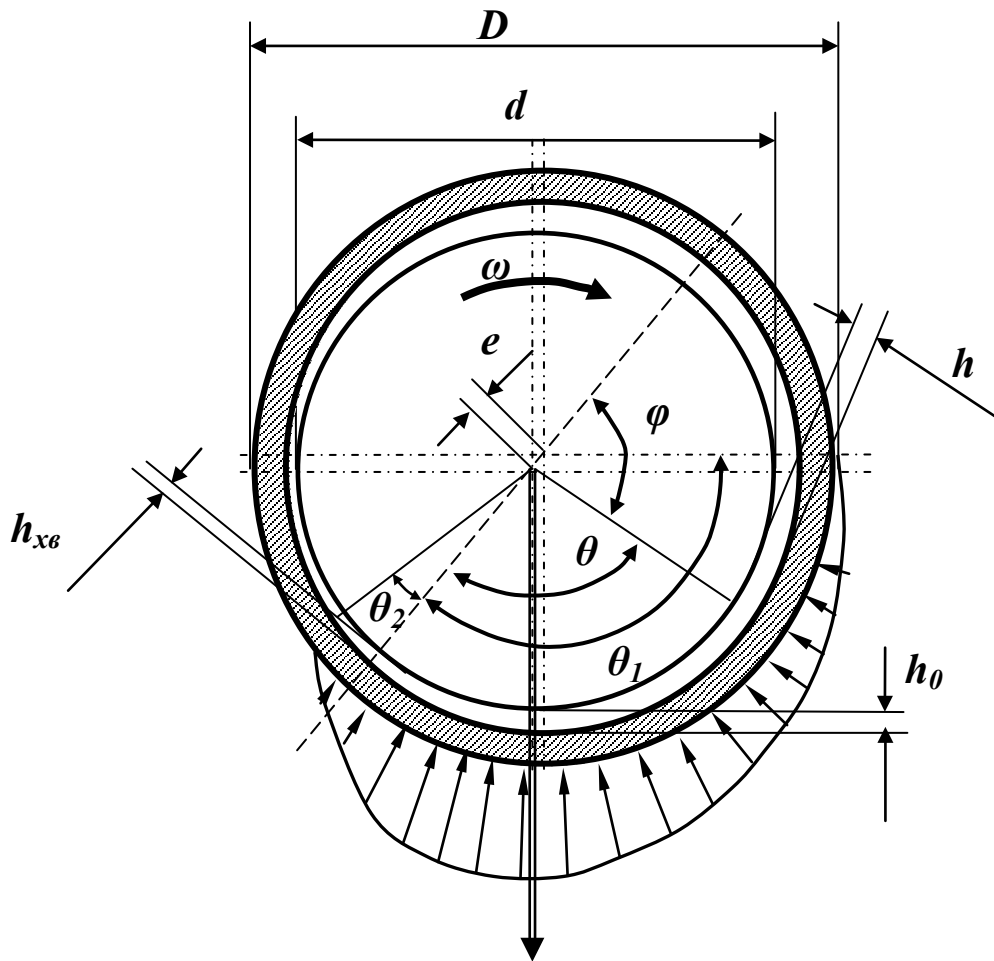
Розрахункова схема підшипника ковзання
